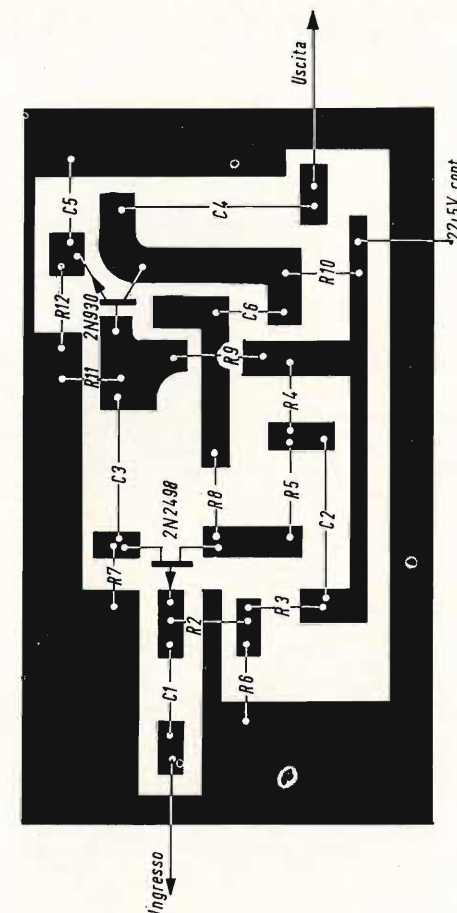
Circuito stampato adatto per il montaggio di fig. 3.
